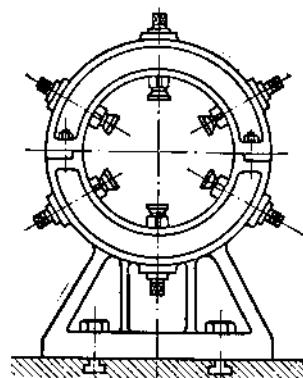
Приспособление для крепления втулки при чистовой расточке.
